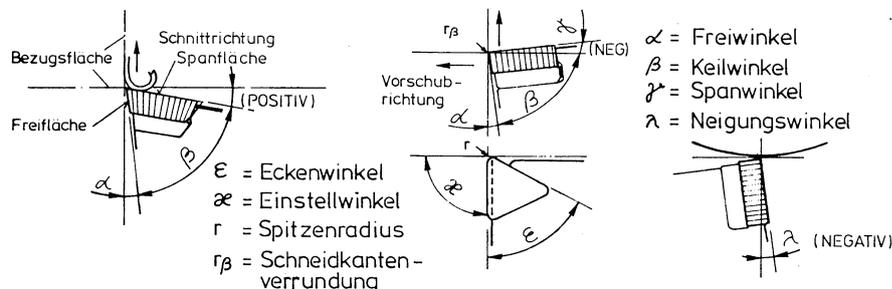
Werkzeugwinkel am Schneidkeil (Schneidengeometrie)
